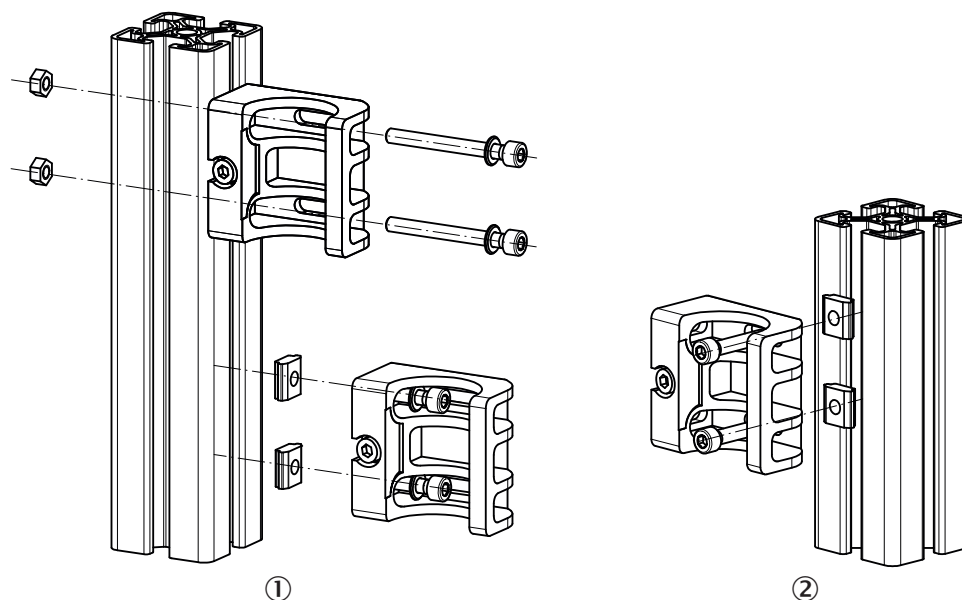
Монтаж креплений FlexFix на раме профиля
